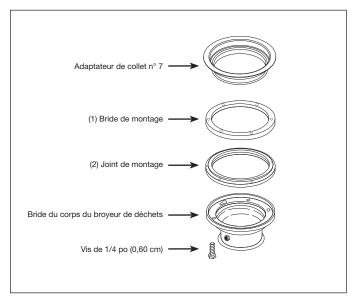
Ensemble de montage n° 7 ou de bol d'évier
